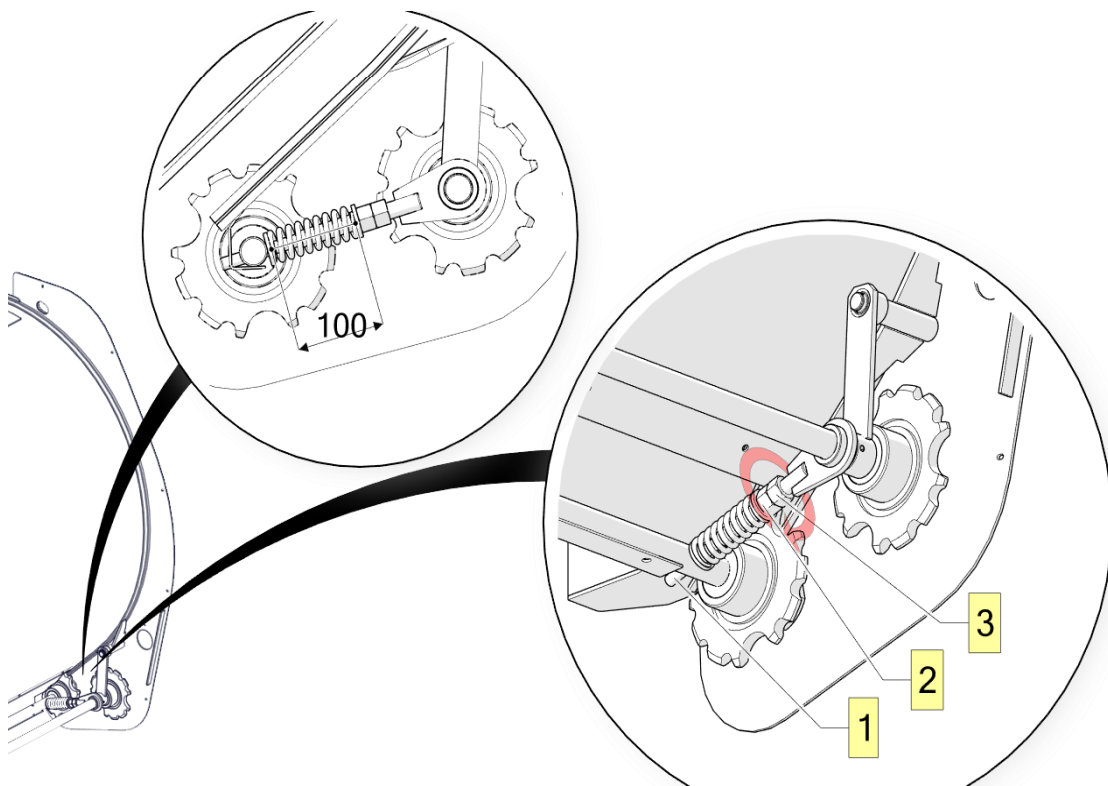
Регулировка натяжения цепно-пруткового транспортера
